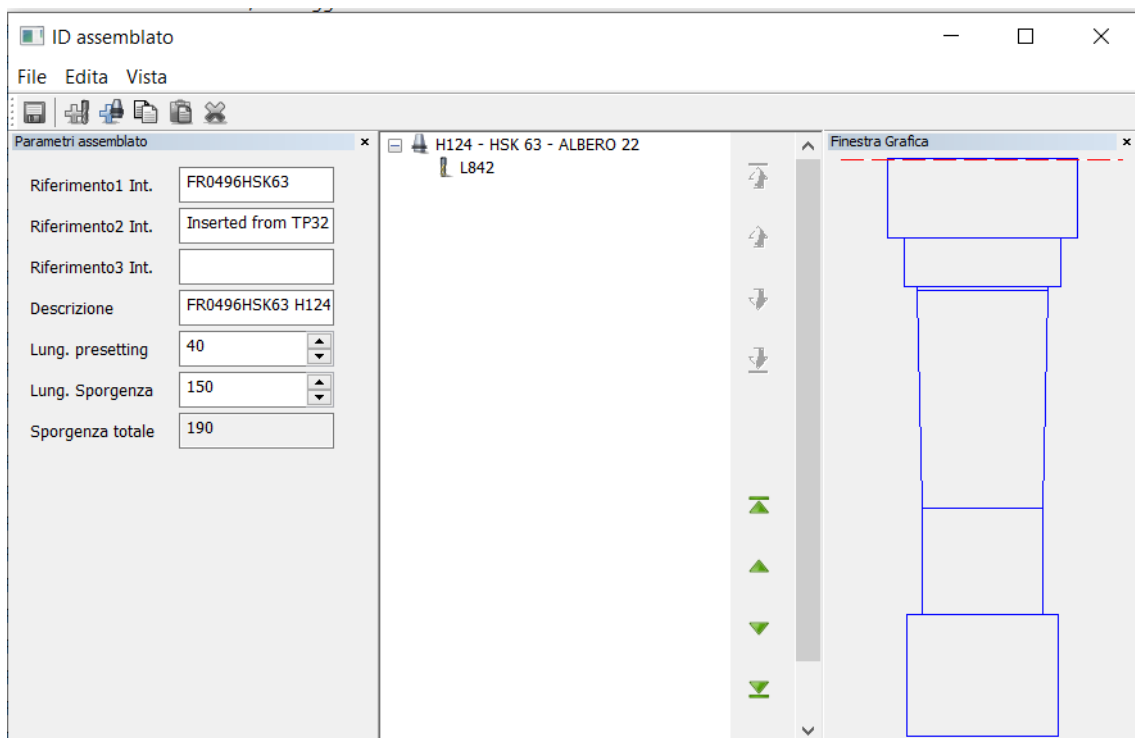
Composizione assemblato utensile FR0496HSK63 nel database di Visi CAM.
